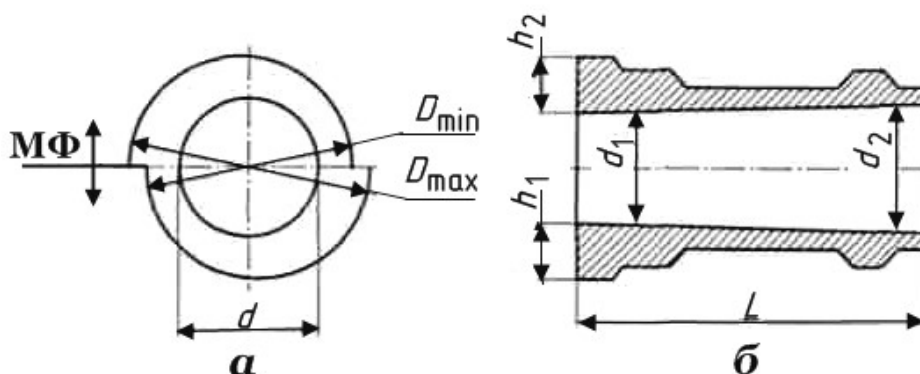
Контроль размеров отливки гильзы: а – контроль наружного диаметра отливки с учетом смещения элементов отливки; б – контроль размеров отливки с учетом погрешностей конусности, разностенности; d – внутренний диаметр отливки; D_{max} , D_{min} – минимальный и максимальный диаметр из-за смещения по плоскости разъема; d_1 , d_2 , h_1 , h_2 – контролируемые внутренний диаметр и толщина стенок отливки
